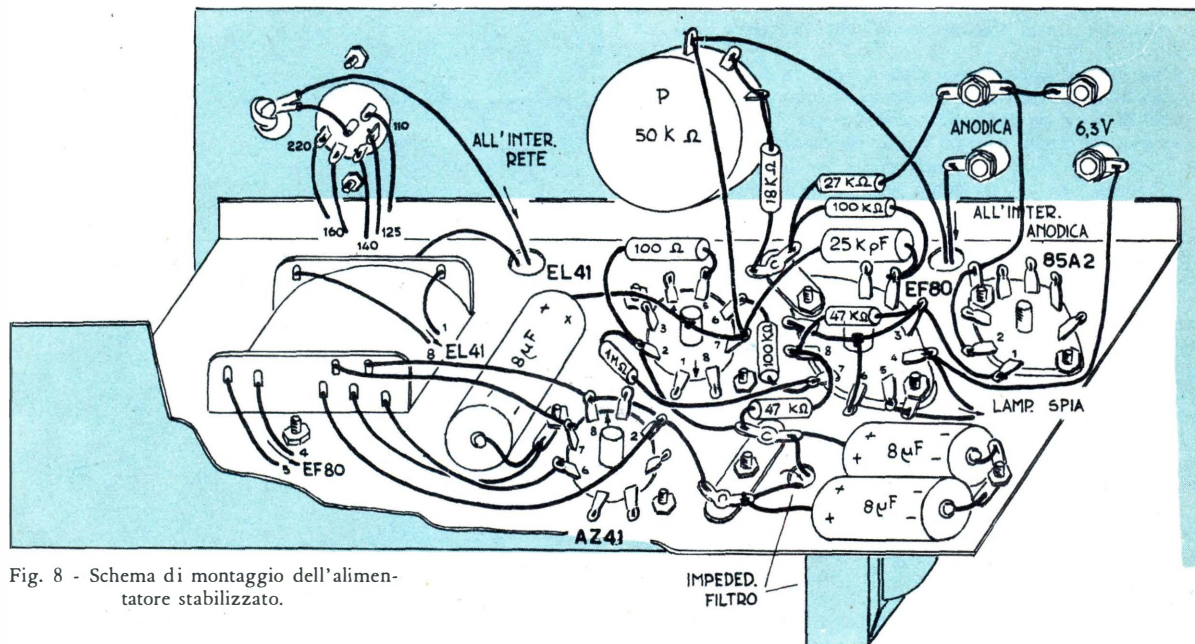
Schema di montaggio dell'alimentatore stabilizzato.
